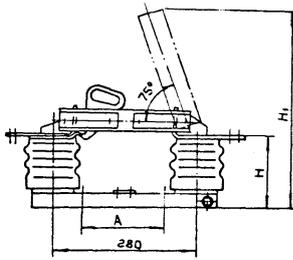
Разъединитель однополюсный типоразмера РВО 10-11/630-1000 УХЛ2, Т2
